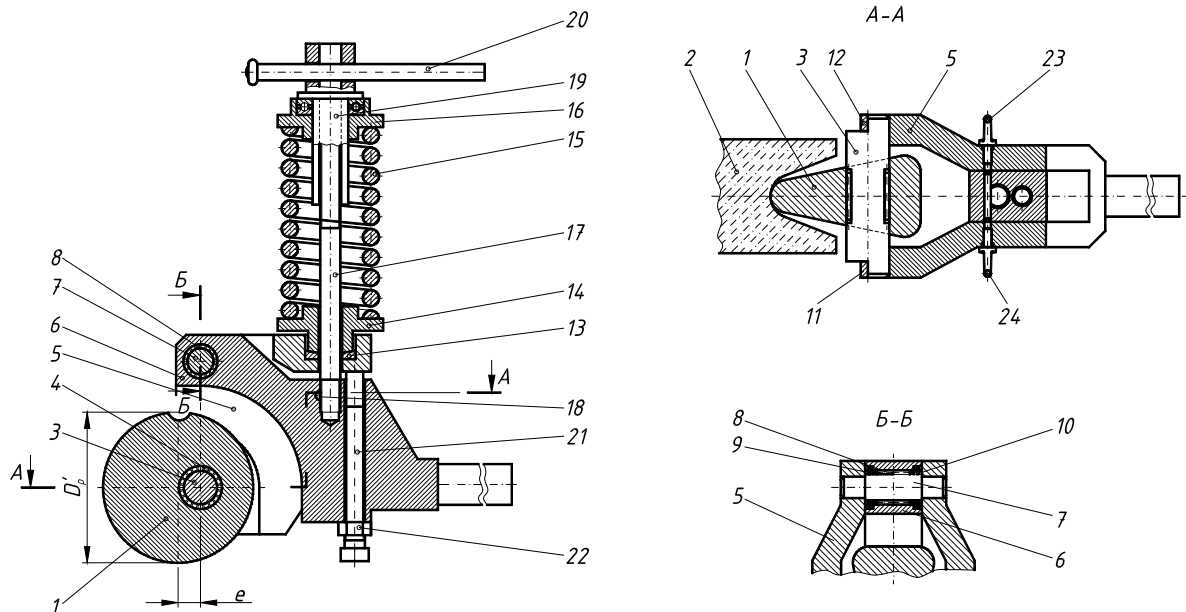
Устройство для обкатывания канатных блоков клиновым роликом: 1 — ролик; 2 — обкатываемая деталь; 3, 7 — ось; 4, 8, 9, 10 — подшипники; 5 — рычаг; 6 — кронштейн; 11, 12 — планки; 13 — сферическая шайба; 14 — втулка; 15 — пружина; 16 — втулка; 17 — тяга; 18 — штифт; 19, 22 — гайка; 20 — рукоятка; 21 — винт; 23, 24 — рымболты
